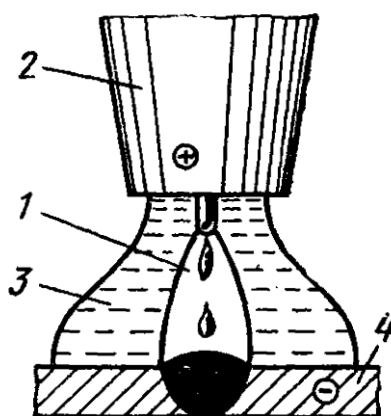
Схема выполнения автоматической сварки под флюсом
